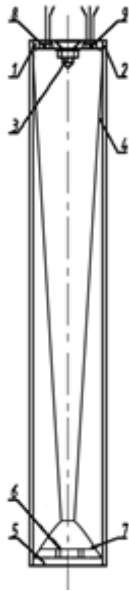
, схема ТТ: 1-верхняя крышка; 2-цилиндрический корпус ТТ; 3- запорный узел; 4-капиллярно-пористая вставка; 5-нижняя крышка; 6-инжекторные каналы; 7-капиллярно-пористый испаритель; 8,9-емкостные датчики конденсации, измеряющие толщину пленки жидкого конденсата.. В качестве рабочей жидкости применен эфир диэтиловый $C_4H_{10}O$ с температурой кипения при атмосферном давлении $T_B = 308.65K$ ($35.5^\circ C$), критические параметры $T_C = 466.55K$ ($193.4^\circ C$), $P_C = 3.61MPa$.
